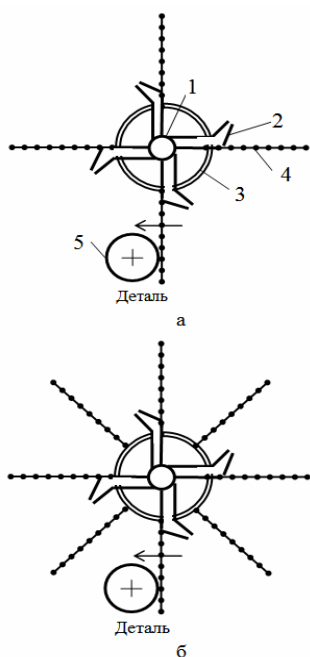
Схема інструменту комбінованої дії для очищення складних поверхонь: а – інструмент із чотирма гнучкими елементами; б – інструмент, що об'єднує гідроструменеву та механічну обробку
